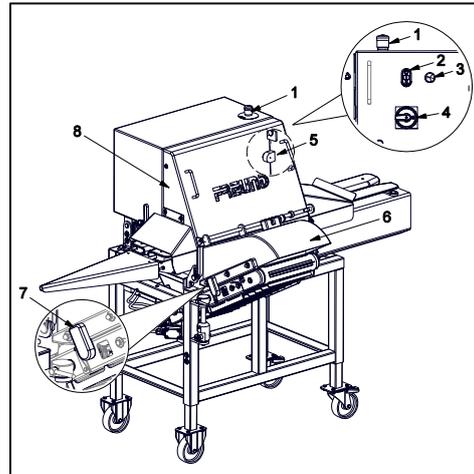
autocollant de sécurité sur les faces avant et arrière de la machine
